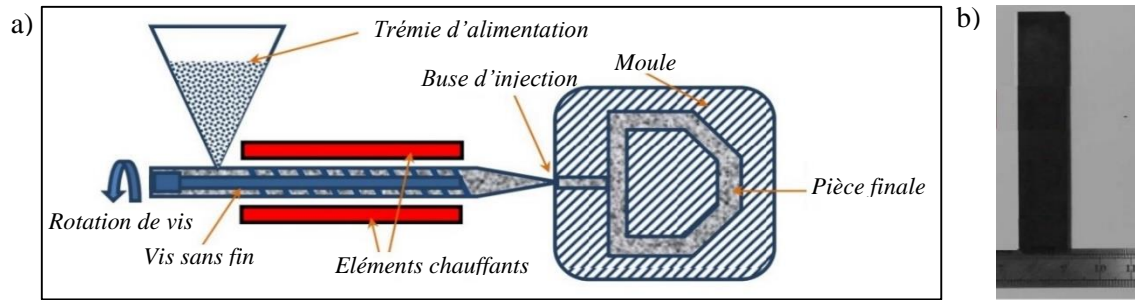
a) Schéma du procédé de mise en forme par moulage par injection [64]; b) Éprouvette injectée à base de poudres magnéto-caloriques [2].
